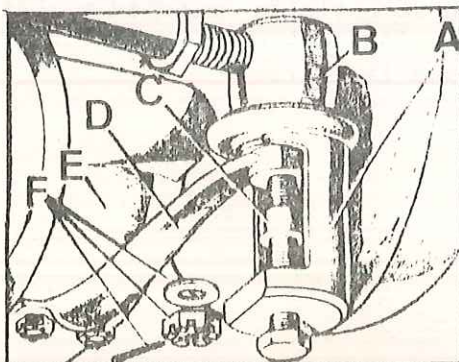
Conexión de la barra de acoplamiento y barra transversal al cárter del pivote de mangueta
